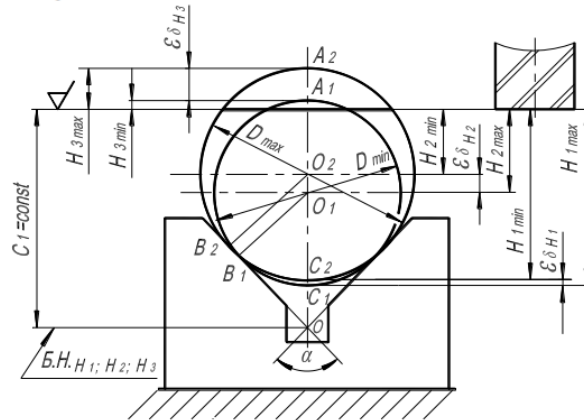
Схема установки заготовки типу вал на призму [9, с. 15]
